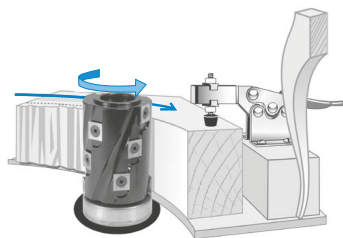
Exemple d'usinage avec un calibreur et son roulement de guidage
